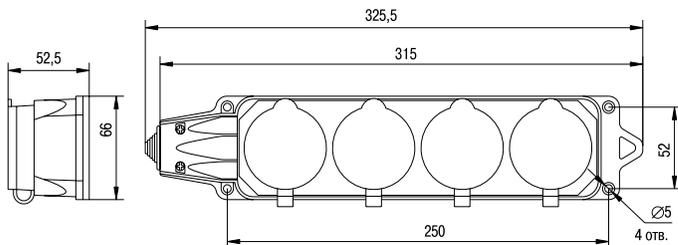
Розетка (колодка) четырёхместная с защитными крышками РКП16-004
